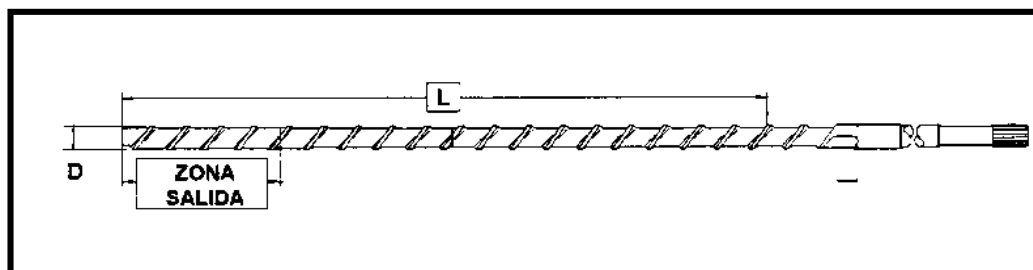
Zona de salida (transición o compresión) del tornillo de inyección.
